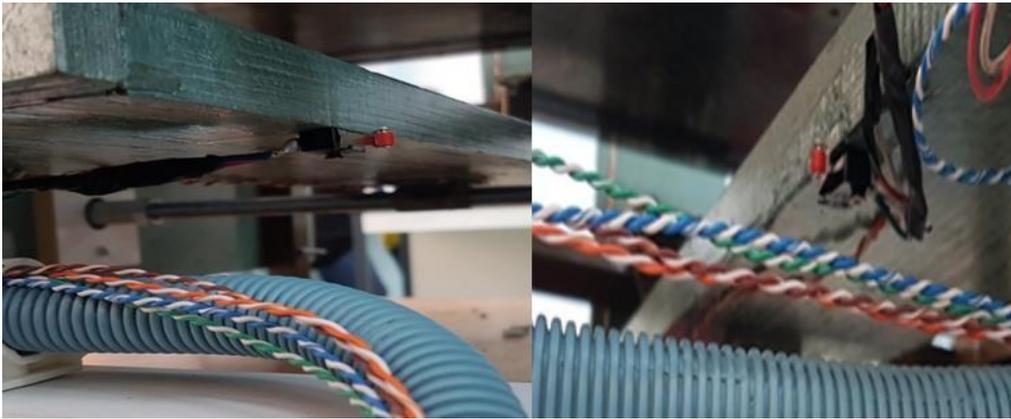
20 : les emplacements des fins de course axe-X, Machine, avant et arrière.
